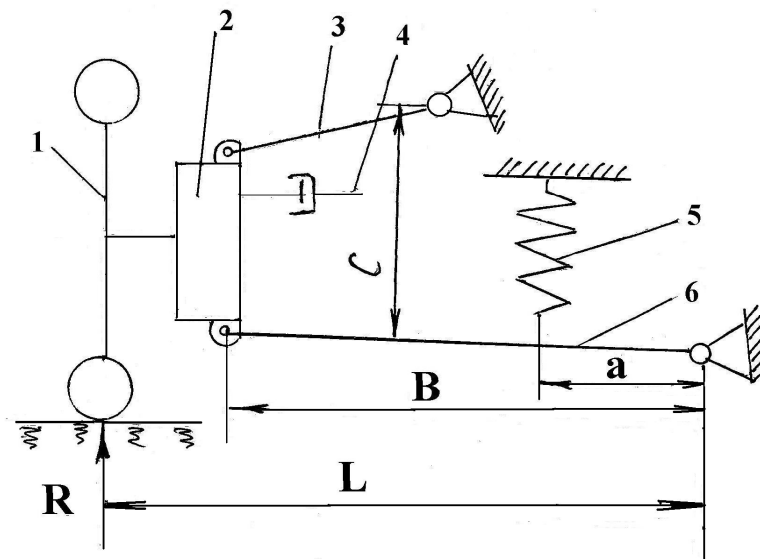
Схема для вибору основних розмірів направляючого пристрою незалежної підвіски передніх коліс: 1 – ведуче колесо; 2 – колісний редуктор; 3 – верхній важіль направляючого пристрою; 4 – карданна передача; 5 – пружний елемент; 6 – нижній важіль направляючого пристрою підвіски.
